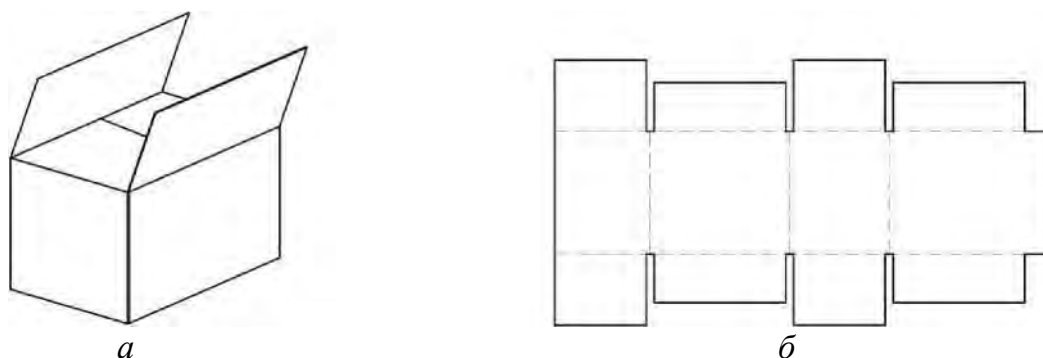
Внешний вид (а) и развертка (б) ящика с четырьмя клапанами
